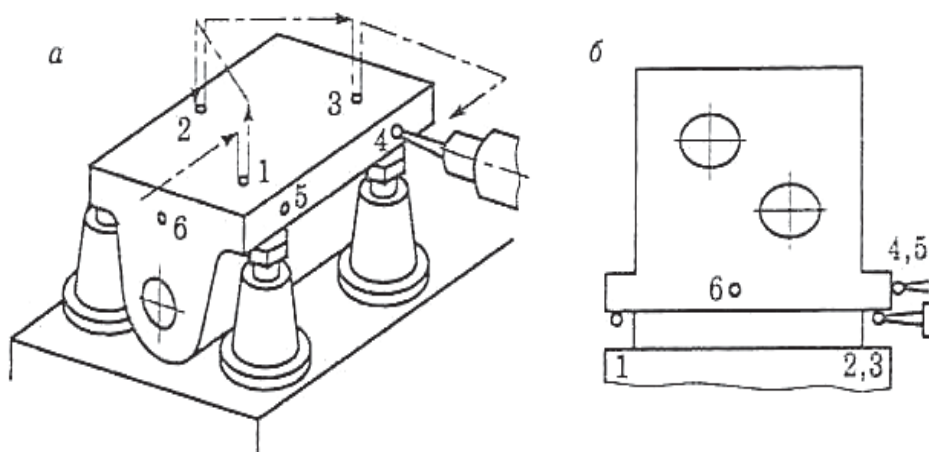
Измерение точности положения заготовки корпусной детали на многоцелевом станке: *а* – базирование заготовки на винтовых регулируемых упорах; *б* – базирование заготовки на подкладной плите
